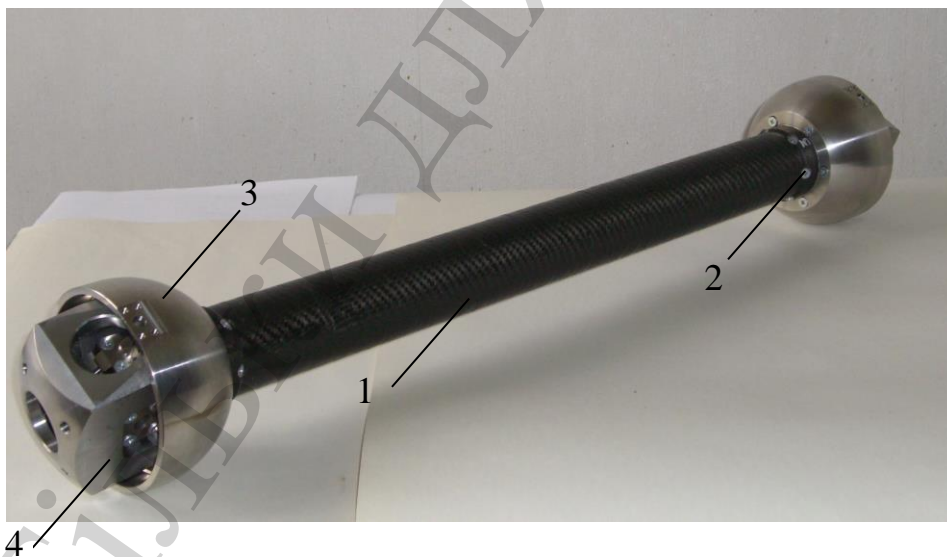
Штанга маніпулятора із встановленими на її кінцях сферичними опорами: 1 – труба; 2 – гвинти; 3 – кожухи; 4 – корпуси опор
